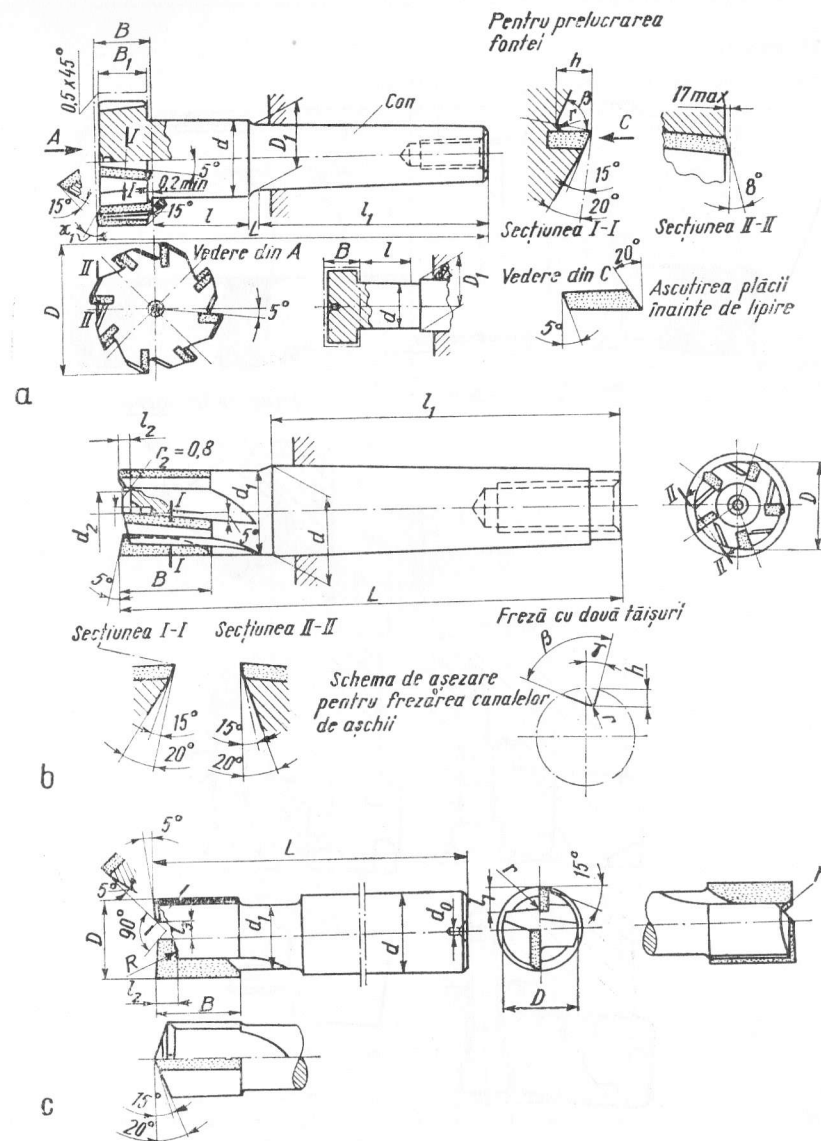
Freze cu plăcuțe din carburi metalice:
